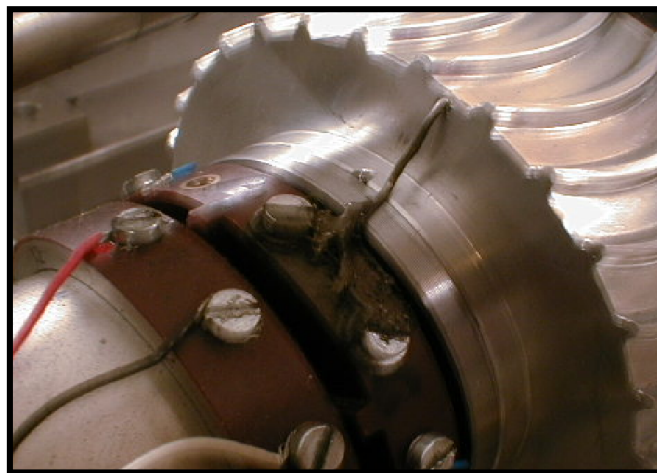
Vue du thermocouple dans la dent de la poulie motrice.
